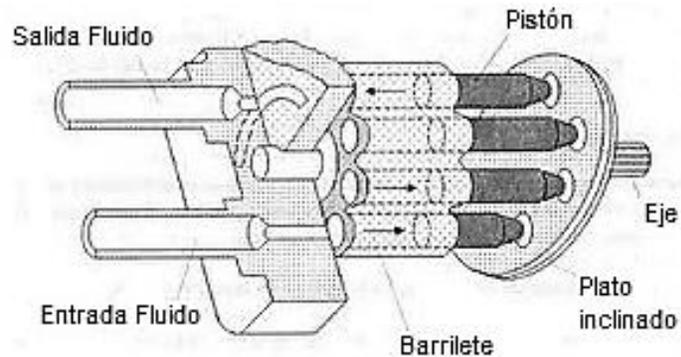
Motor de Pistón Axiales de Desplazamiento Variable.
